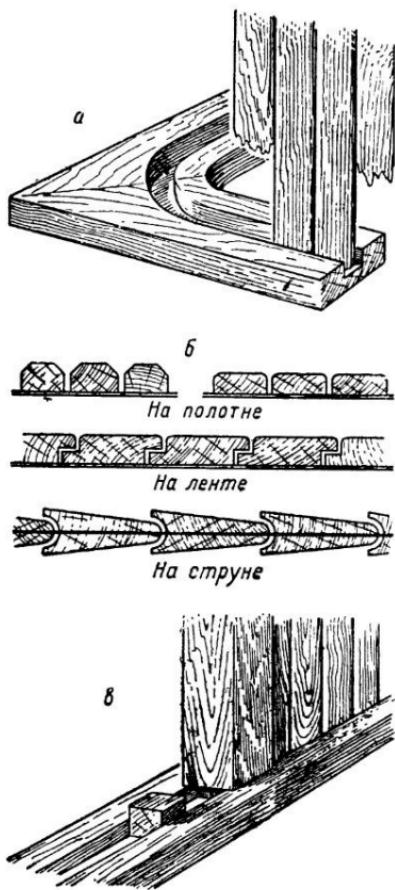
Жалюзи: а — устройство нижней канавки; б — сечения реек; в — двусторчатое жалюзи.
